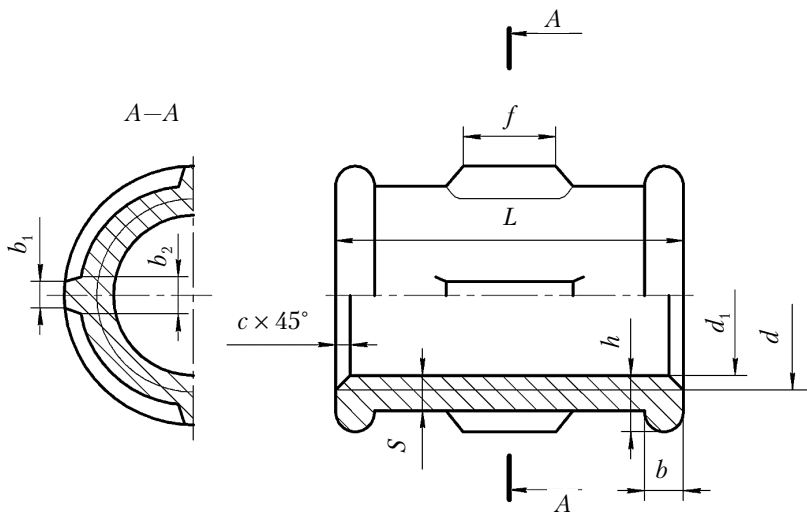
Соединение труб муфтой с цилиндрической резьбой
